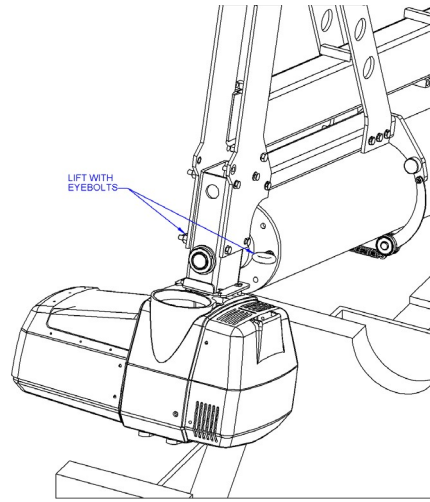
E. Rimozione del gruppo Easy Arm® dall'imballaggio.
